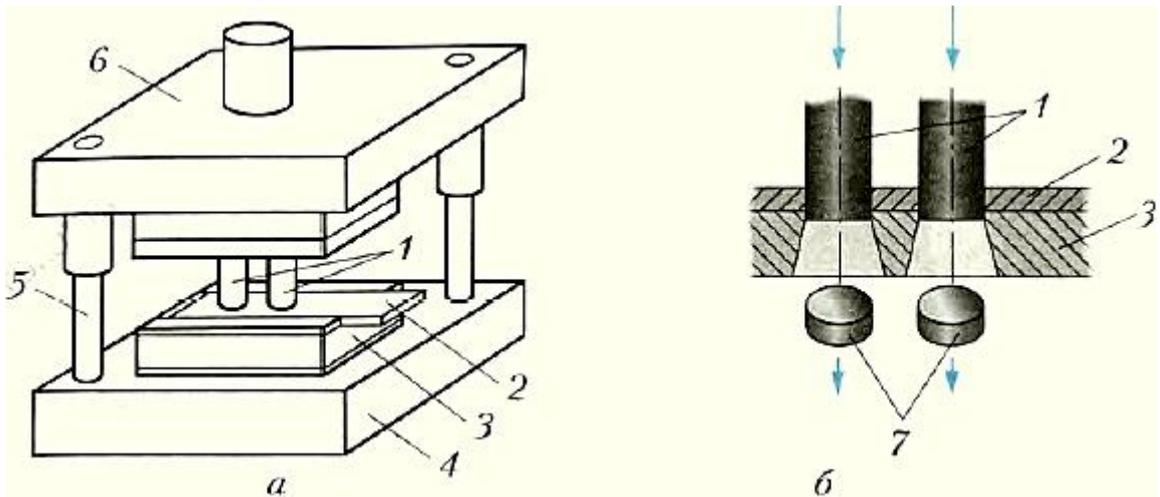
Общий вид штампа (а) и процесс пробивания отверстий (б): 1 — пуансоны; 2 — заготовка — металлический лист; 3 — матрица; 4 — нижняя плита; 5 — направляющие колонки; 6 — верхняя плита; 7 — отходы
